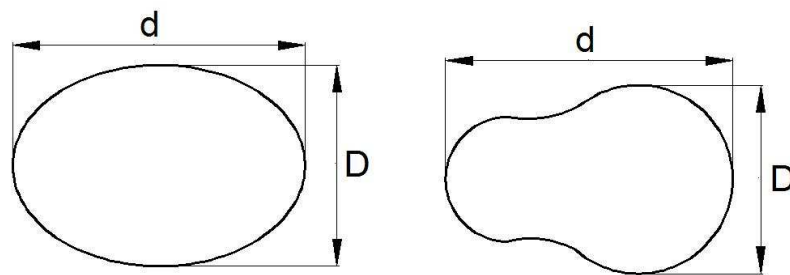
14. Formas de medir el diámetro del punto de soldadura.<sup>5</sup>
